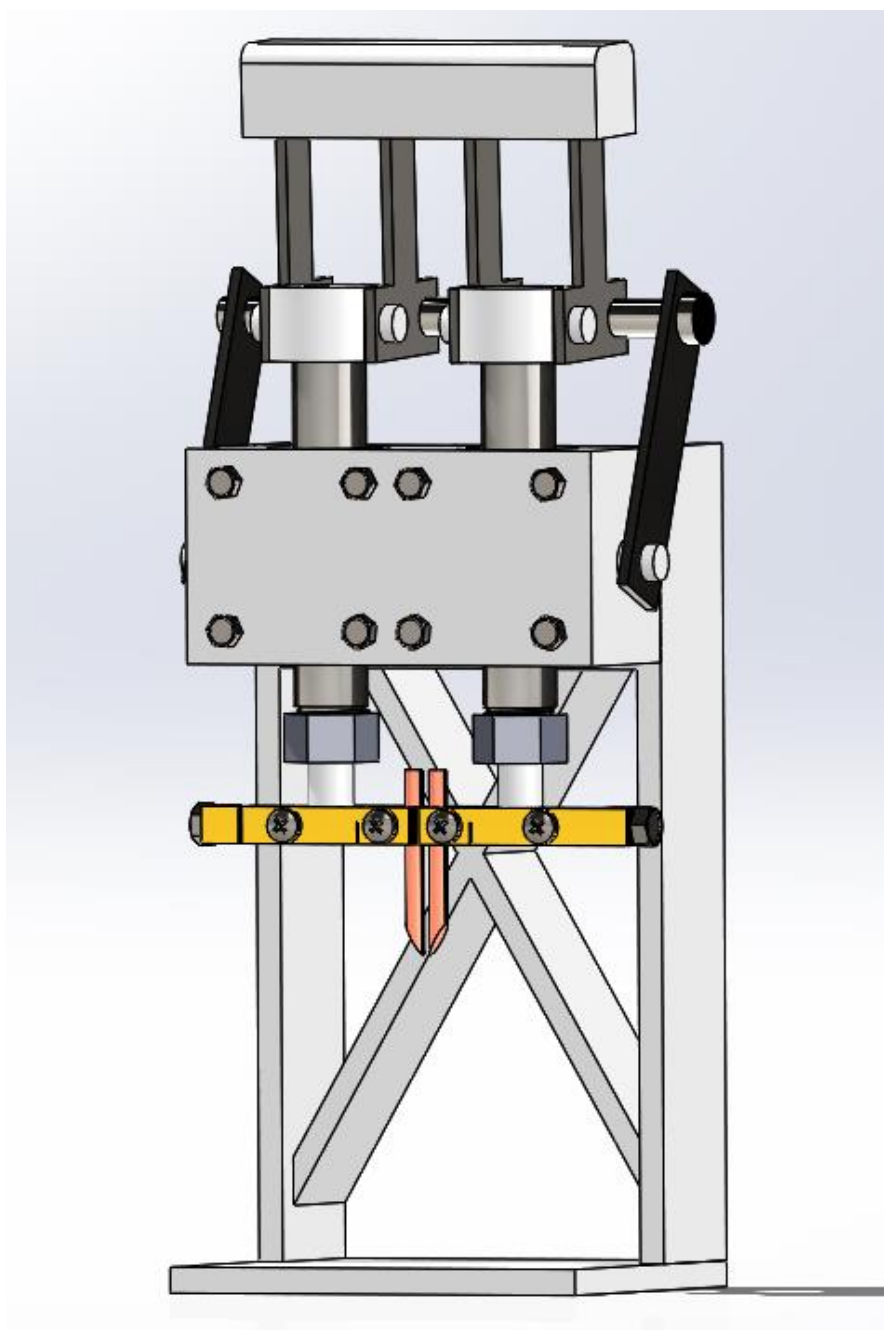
Внешний вид приспособления для микроконтактной точечной сварки
